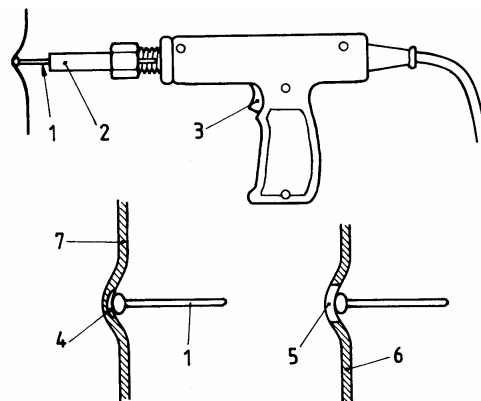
Soldadura de un clavo sobre la lámina de acero deteriorada.
